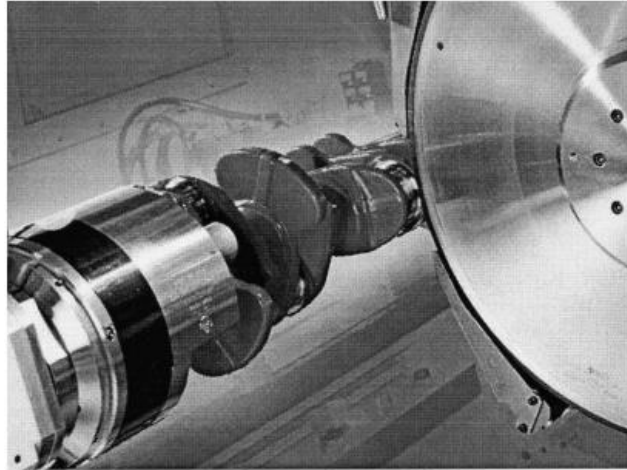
Маятникове шліфування кругами із кубічного нітриду бору
